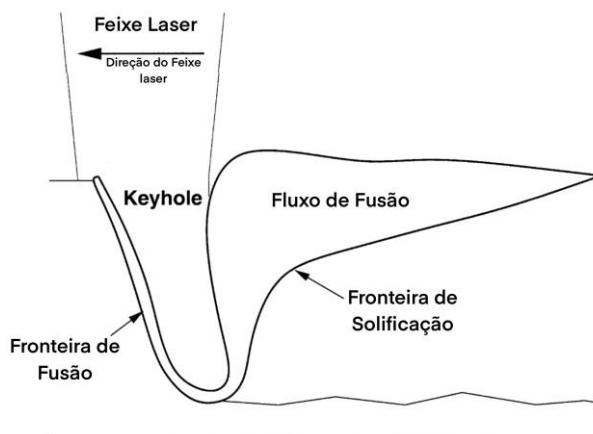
Diagrama da formação de *Keyhole* através do processo de soldadura a laser
